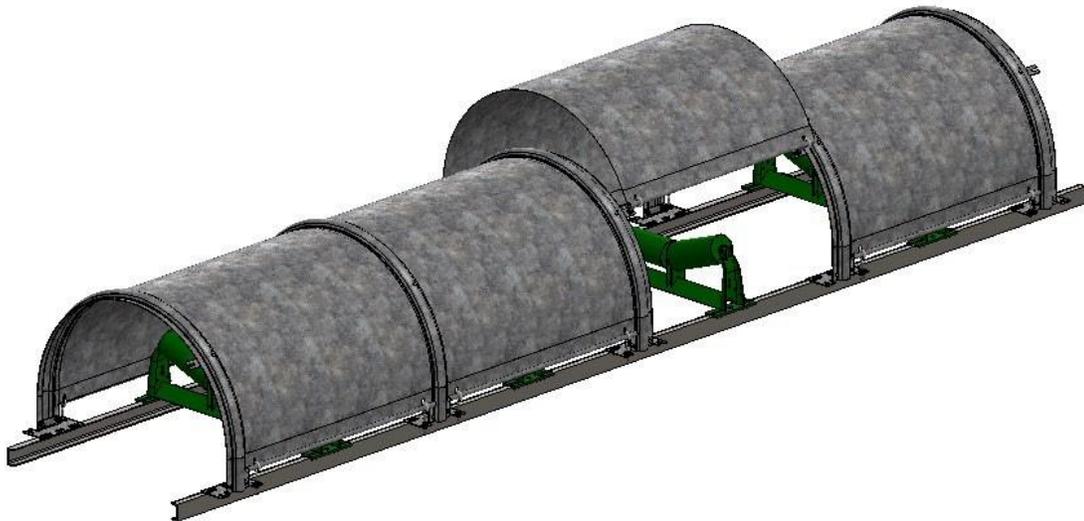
CUBIERTAS COMPLETAS CON UNA SECCIÓN ABIERTA
